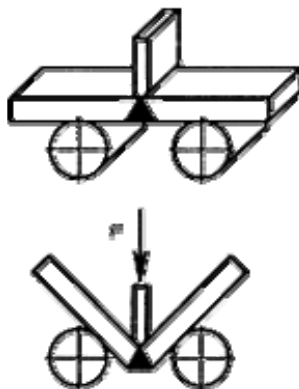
Схема испытания полиэтиленовых образцов на статический изгиб
